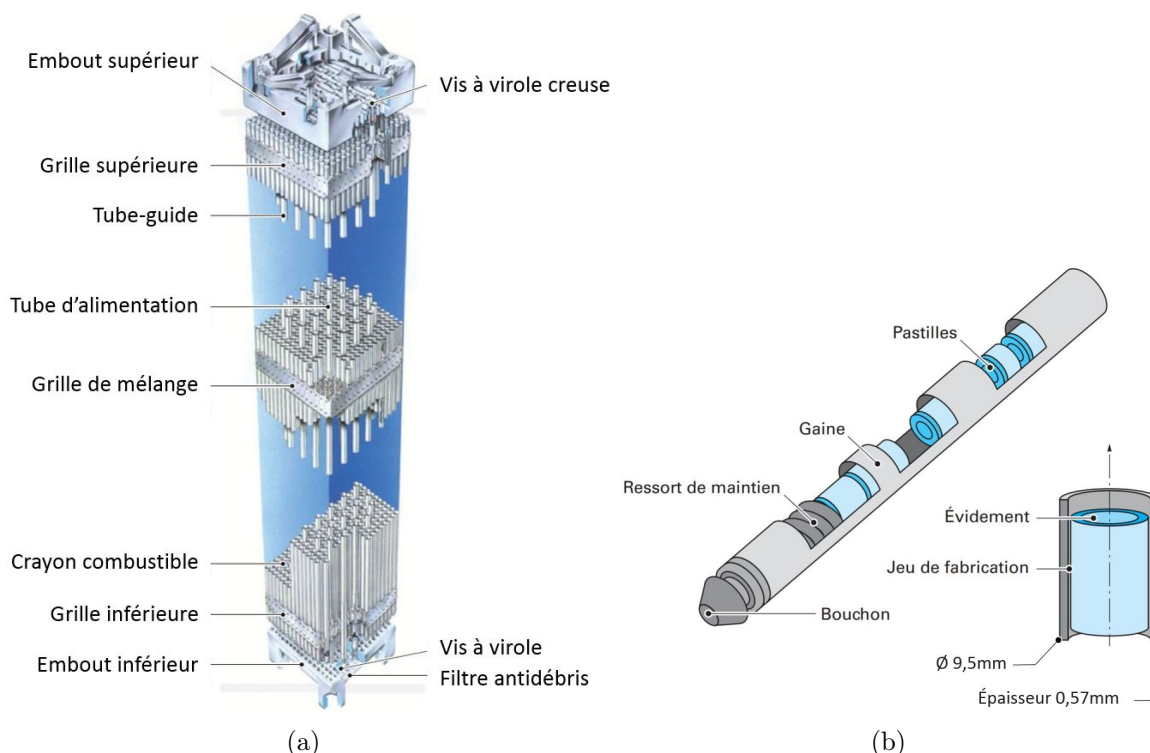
(a) Schéma d'un assemblage; (b) Vue éclatée d'un crayon combustible combustible [27].
